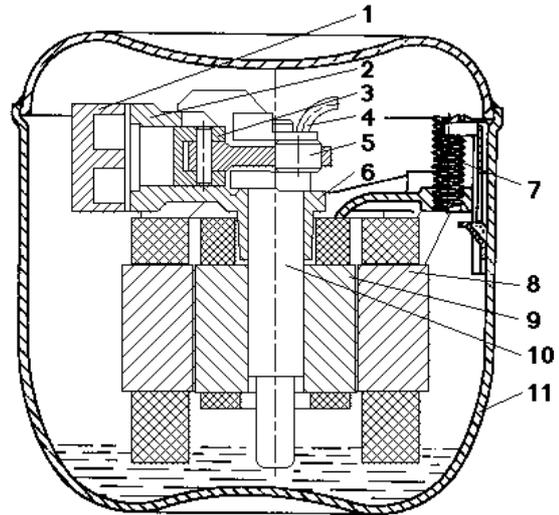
Beispiel für Schallflußmodell: Kältekompressor. 1 Zylinderkopf; 2 Zylinder; 3 Kolben; 4 Schmiereinrichtung; 5 Pleuellager; 6 Pleuellager; 7 Federn; 8 Stator Elektromotor; 9 Rotor Elektromotor; 10 Welle; 11 Gehäuse.
